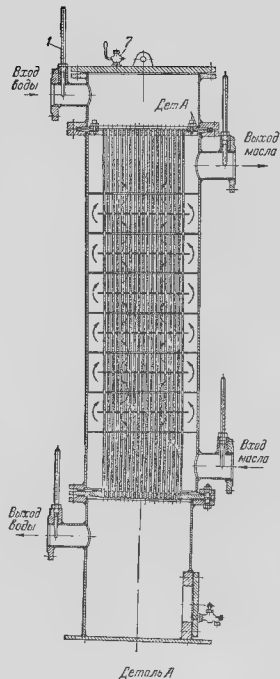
Маслоохладитель ЛМЗ более новой конструкции
